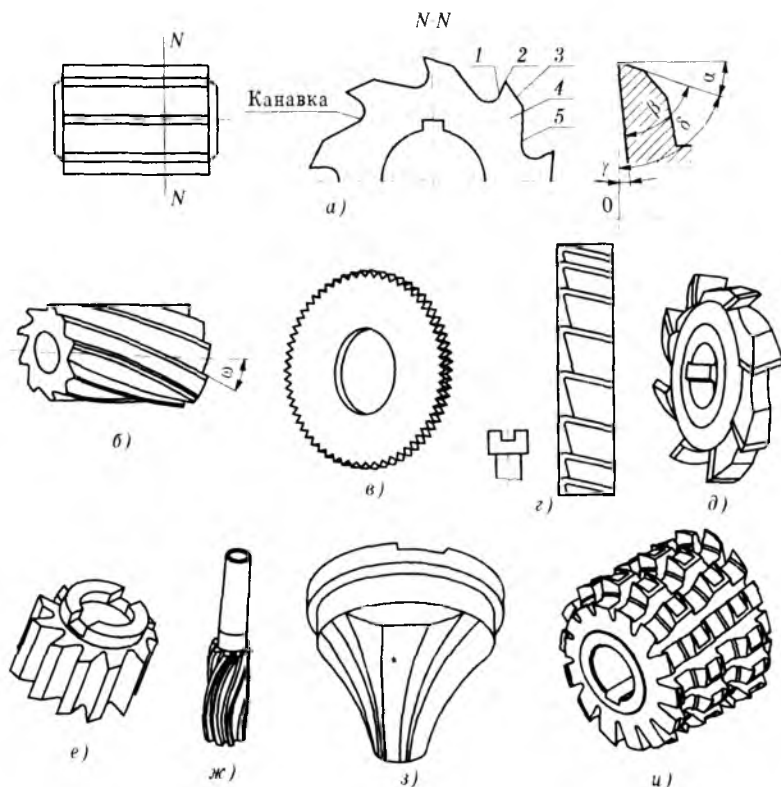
Общий вид инструментов для фрезерования заготовок:
